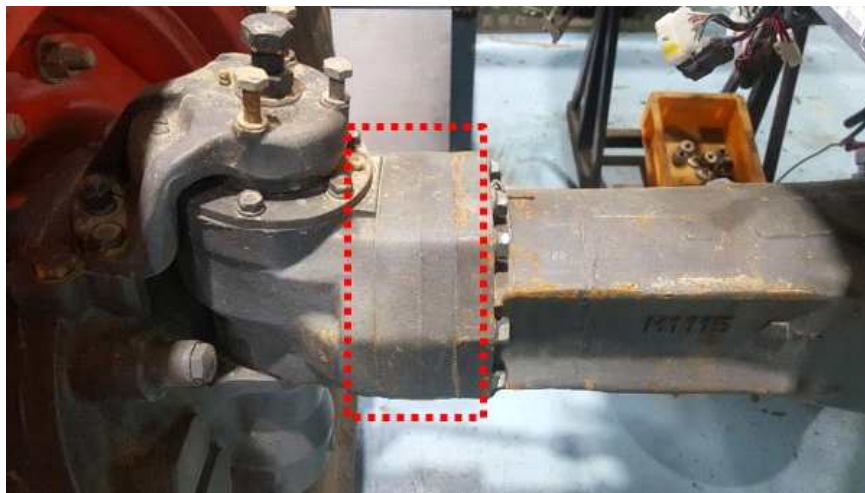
Flange to Flange 조절용 간격통(예시)(K사)
